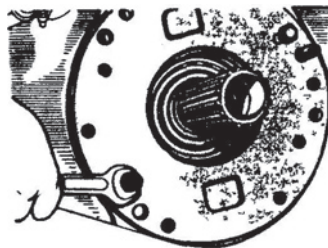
Выпрессовка стакана подшипников в сборе с ведущей шестерней главной передачи.
